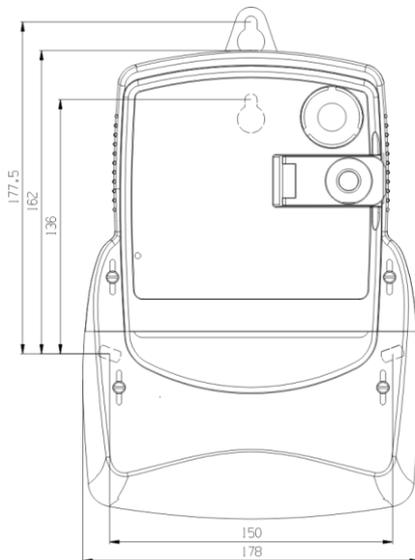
Ausführung mit einer zusätzlichen Aufhängung
